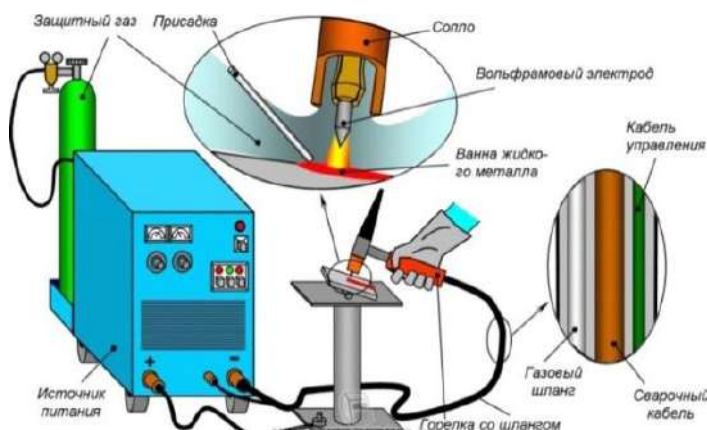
Оборудование для сварки в среде аргона.
